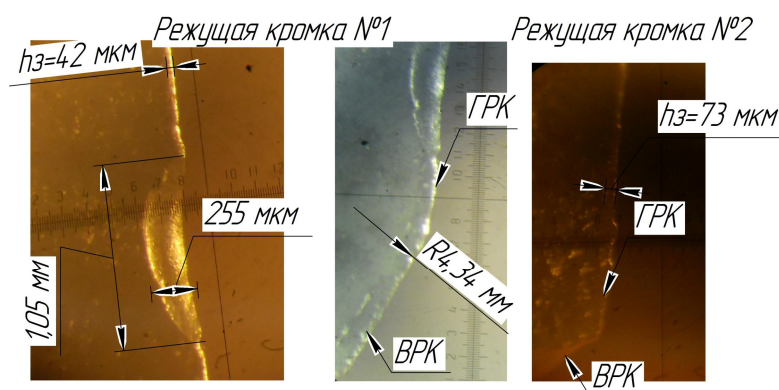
Состояние главных режущих кромок сверла по итогам сверления всех запланированных отверстий
